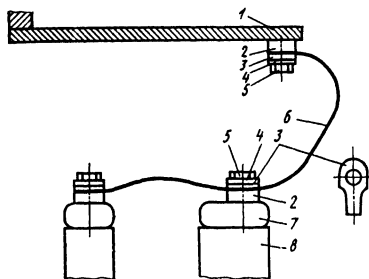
Схема заземления прессующих колец при раздельной прессовке обмоток: 1 — полка ярмовой балки; 2 — бобышка; 3, 4 — стопорная и пружинная шайбы; 5 — болт; 6 — заземляющая шинка; 7 — прессующие кольца обмоток; 8 — обмотки
